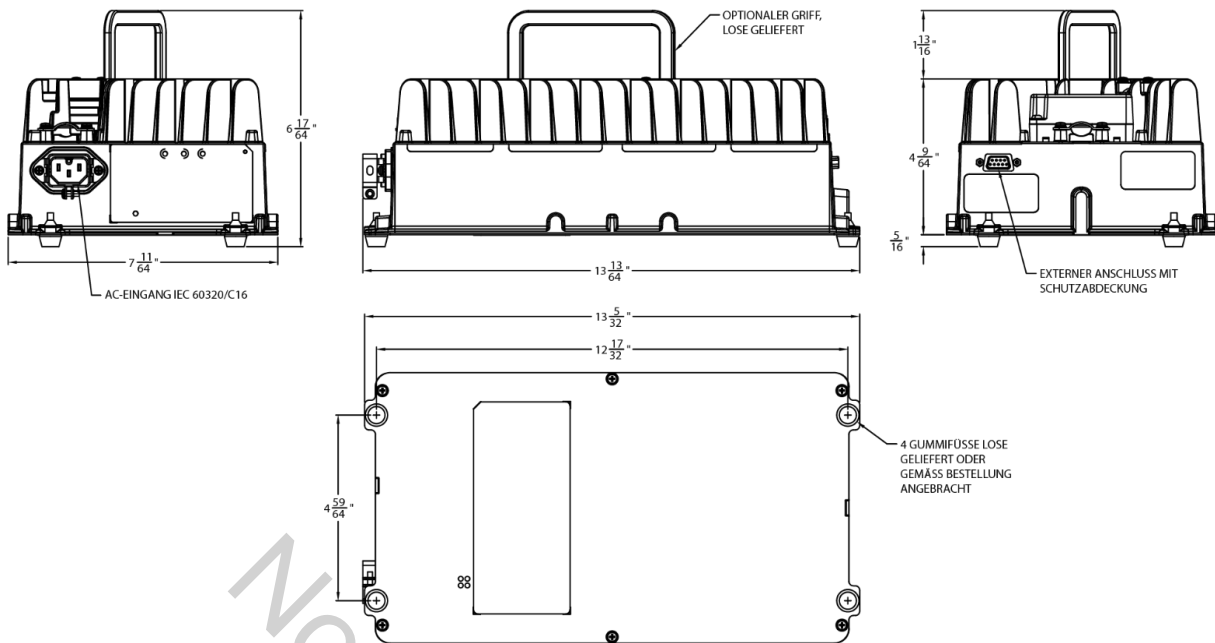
Abmessungen des Ladegeräts und die Positionen der Montagelöcher
